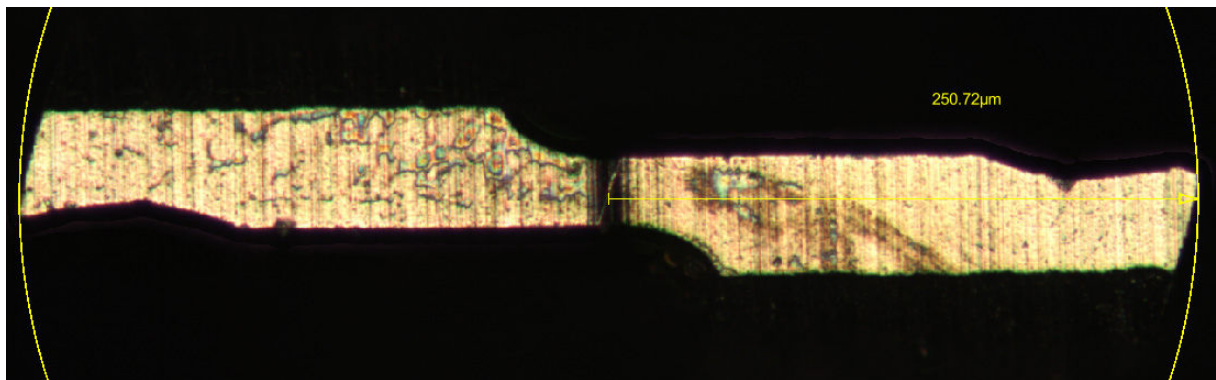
fraise D0.5Z2#27 : vue bout
